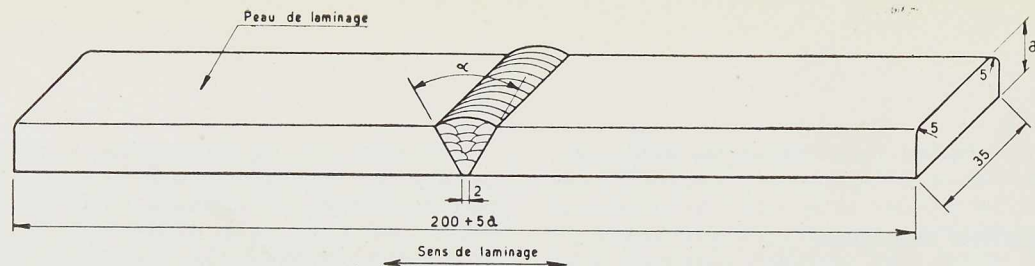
Eprouvette de l'essai de pliage d'un joint soudé.
